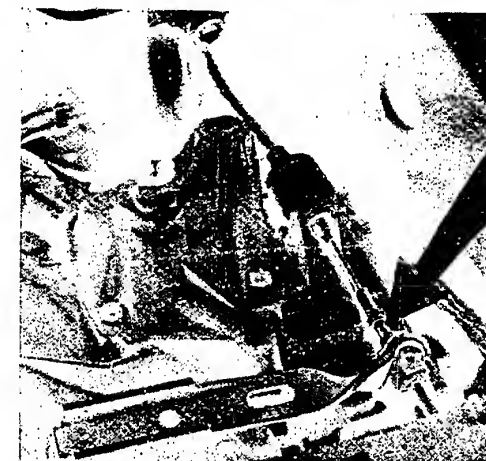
Die Kupplung wird unten im Motorraum am Gewindeteil des Seilzuges eingestellt.
